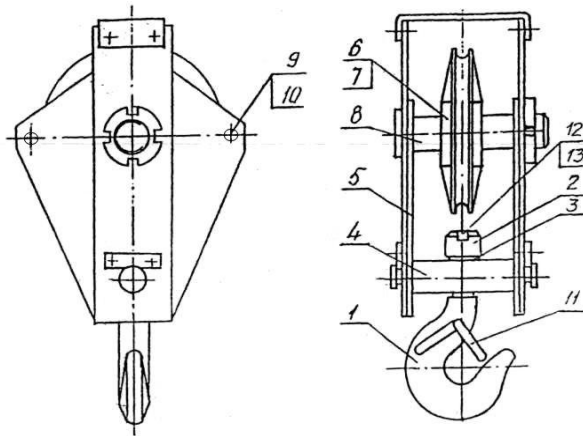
Гакова підвіска: 1 – гак; 2 – гайка; 3 – упорний підшипник; 4 – траверса; 5 – щока; 6 – блок; 7 – підшипник кочення; 8 – вісь; 9 – болт; 10 – дистанційна втулка; 11 – заціпка; 12 – стопорна планка; 13 – болт
